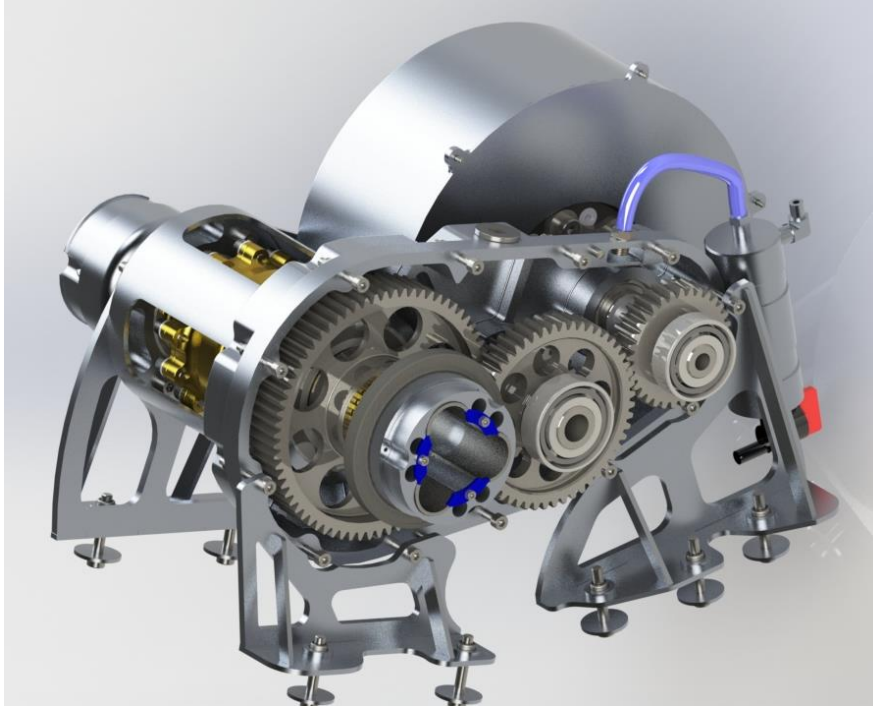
Conjunt motor, transmissió i diferencial del CAT11e
